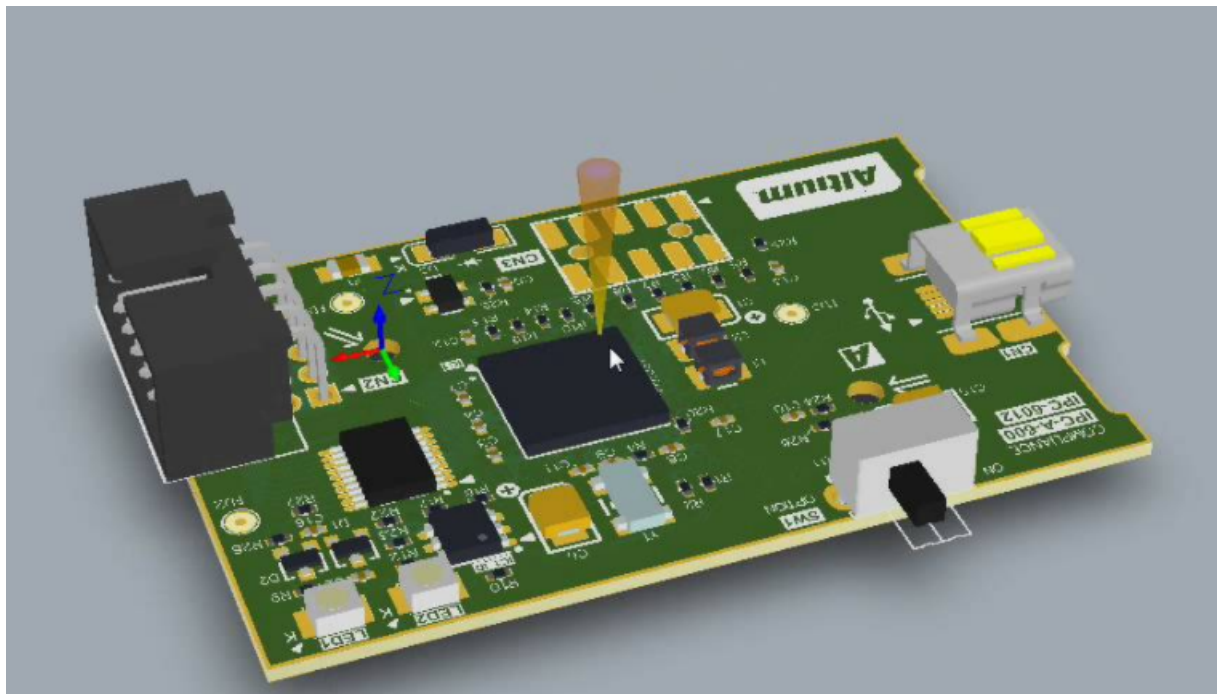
Diseño en 3 dimensiones realizado con Altium Designer.
